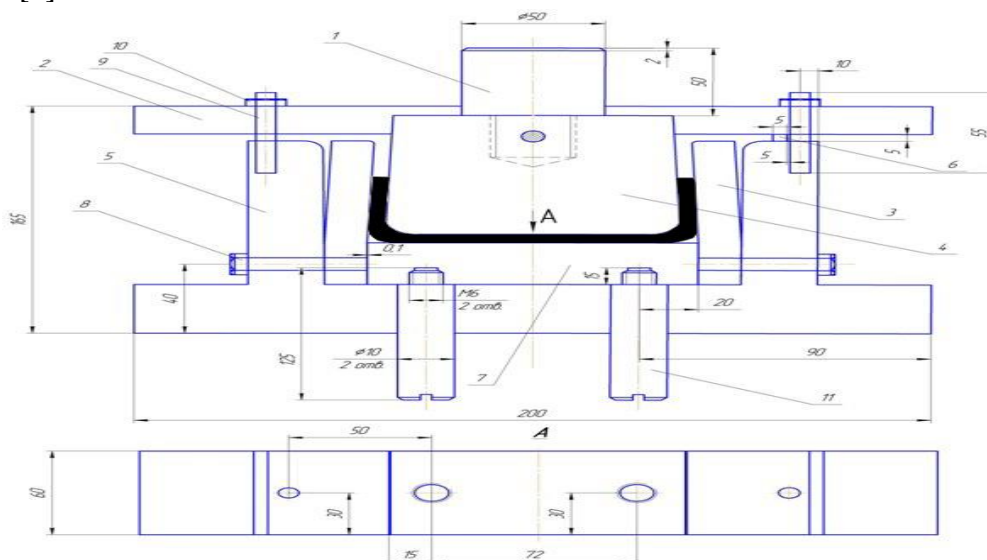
Чертеж штампа: 1 – хвостовик, 2 – верхняя плита штампа, 3 – упругая планка, 4 – пуансон, 5 – матрица (нижняя плита штампа), 6 – упор, 7 – выталкиватель, 8 – соединительный болт, 9 – направляющая верхней плиты, 10 – стопорная гайка, 11 – направляющая выталкивателя
